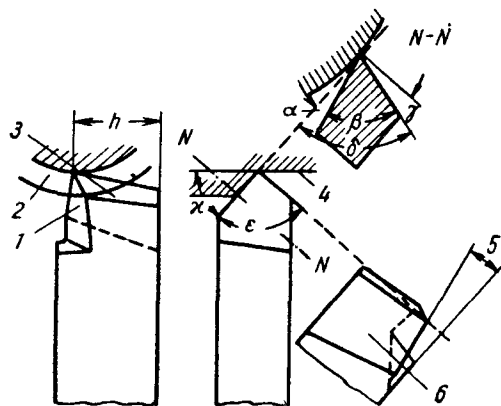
Углы и поверхности токарного резца по стандарту ДИН 768:
